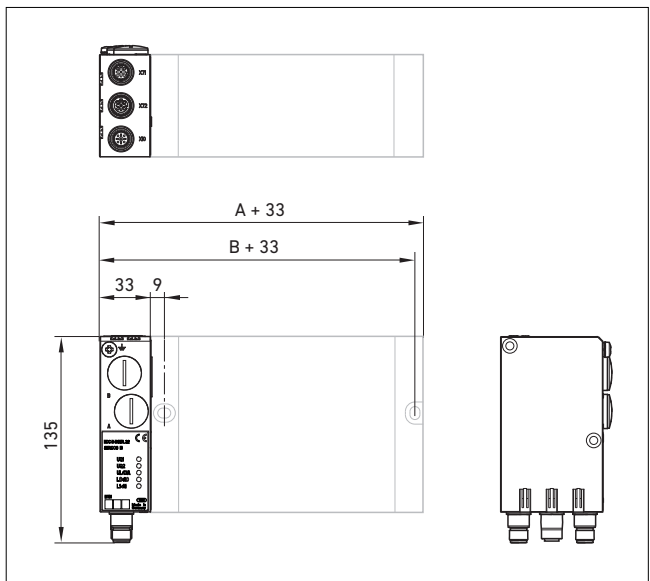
Disegno quotato del sistema di valvole (accoppiatore bus e valvole)
